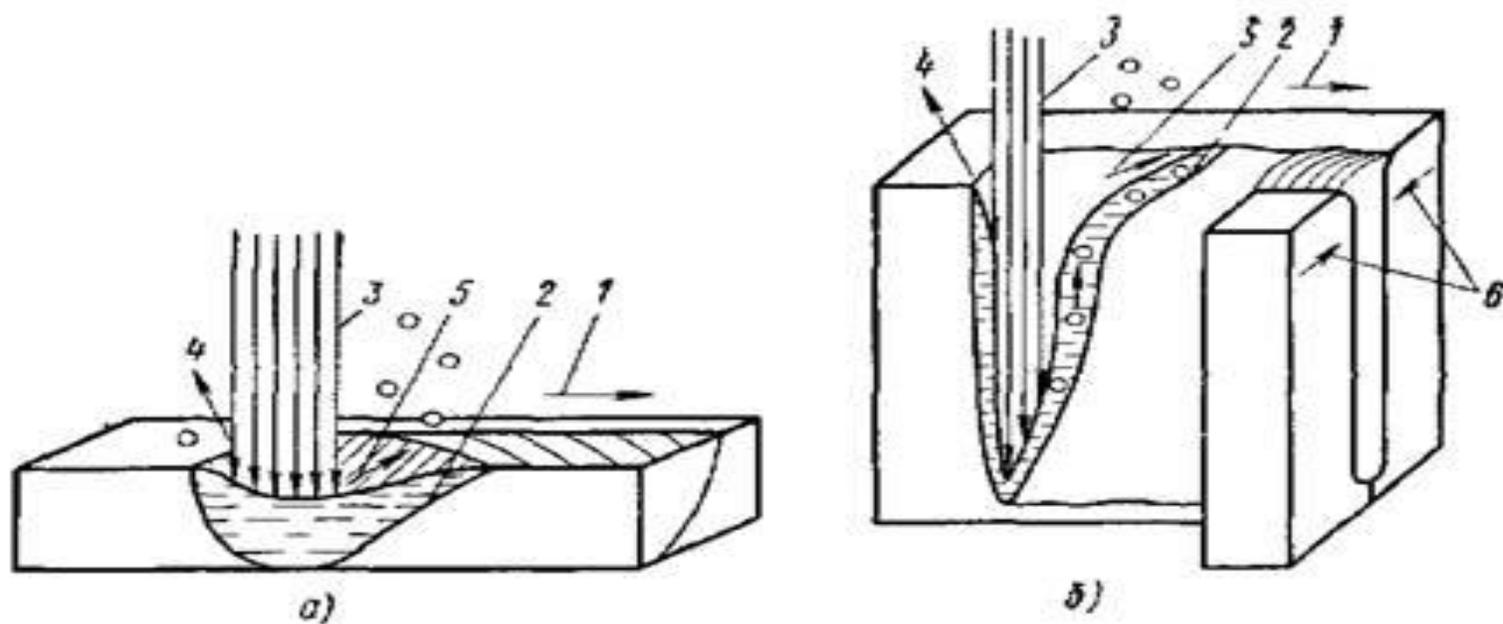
Схема электроннолучевой сварки металлов малой (а) и большой (б) толщины:
